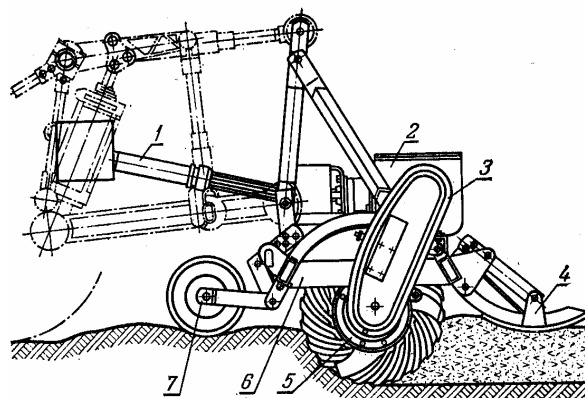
Фреза ФБН-1,5: 1- карданный вал от ВОМ трактора, 2 и 3- редукторы, 4- ограничитель глубины обработки почвы, 5- фрезерный барабан, 6- рама, 7- опорное колесо
